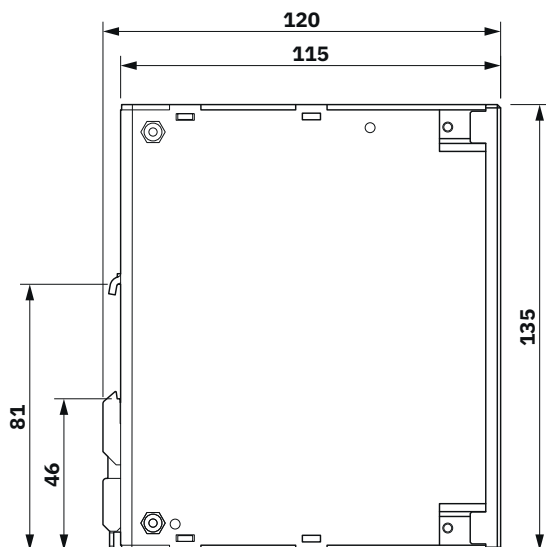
Abmessungen Seitenansicht (Maße in mm)
